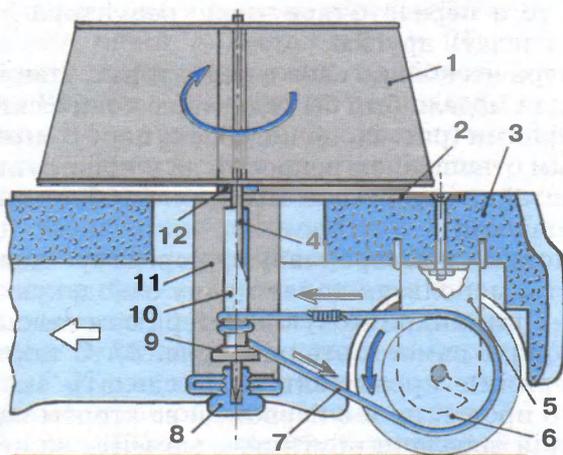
Кинематическая схема ветромобиля: 1 — ротор; 2 — несущая пластина; 3 — нижняя часть кузова; 4 — ось ротора; 5 — скоба крепления заднего моста; 6 — шкив; 7 — пассик; 8 — опорная втулка оси; 9 — направляющая шайба; 10 — резиновая трубка ведущего вала; 11 — кронштейн; 12 — шайба.
